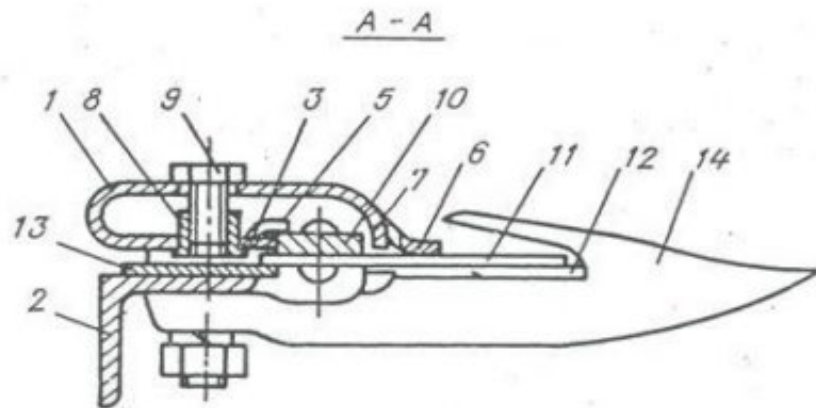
Патент №1607725 «Притискний пристрій ножа ріжучого апарата»
